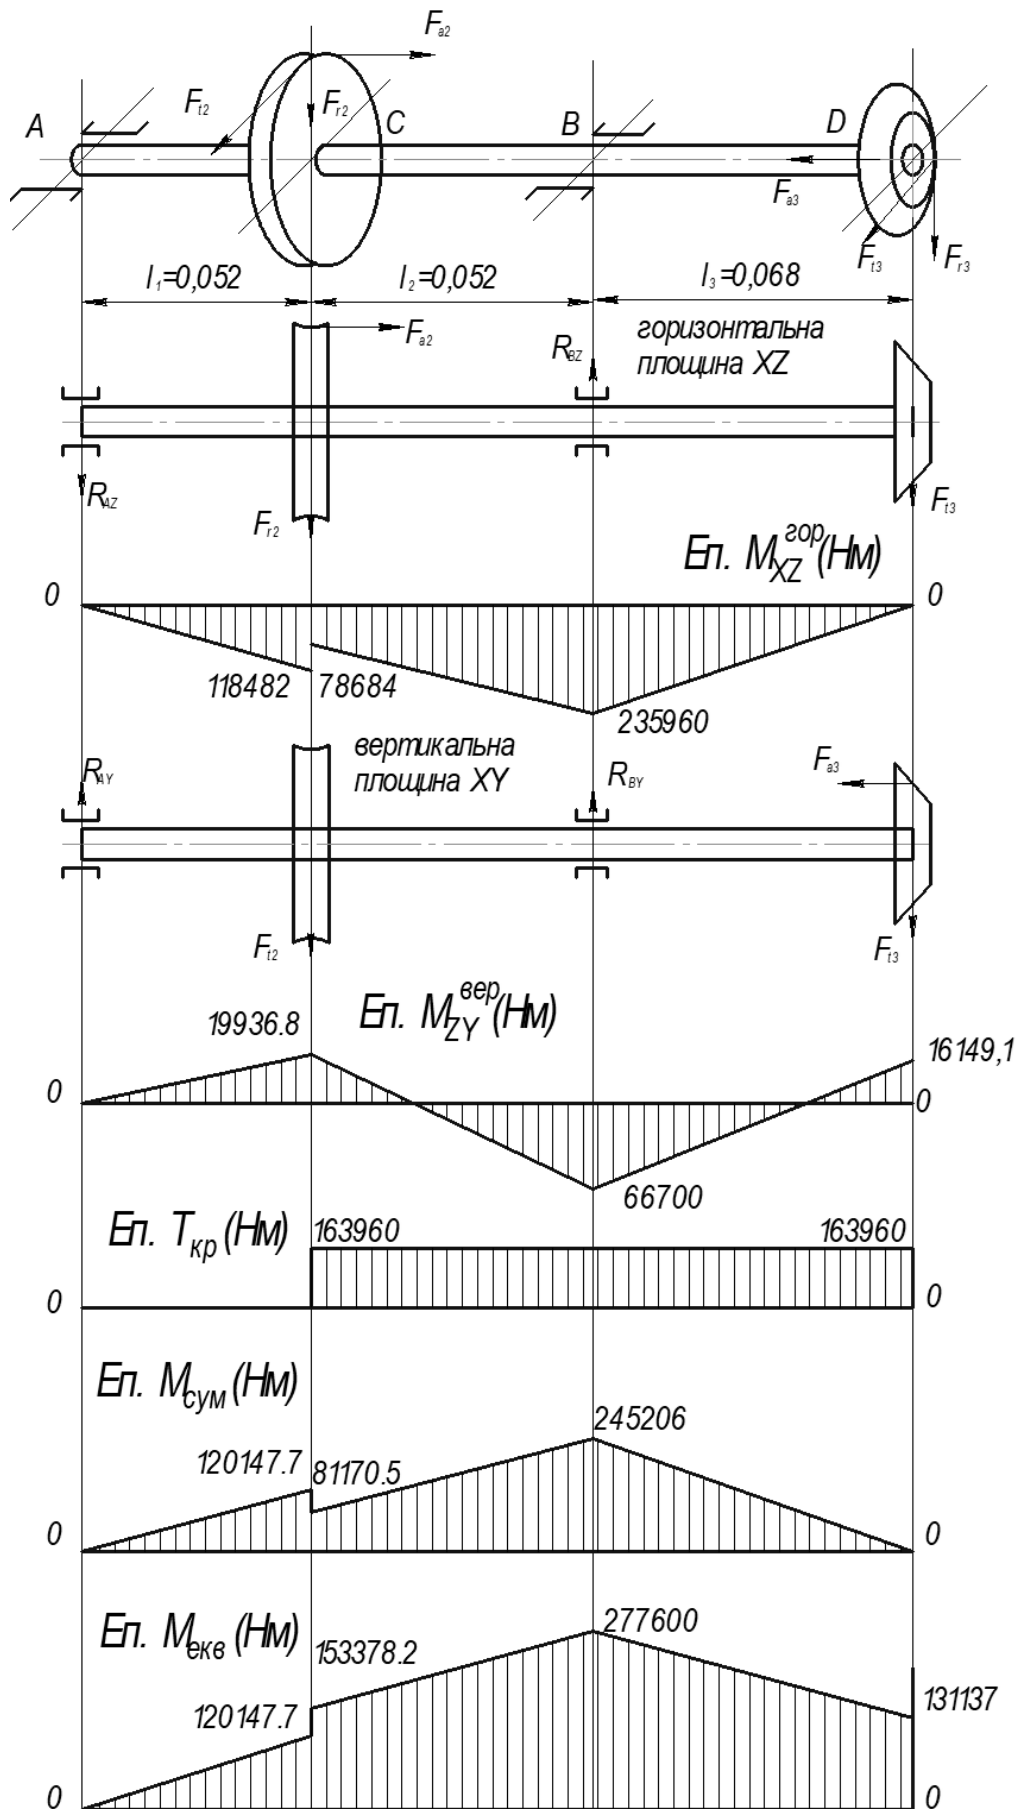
Епюри вала Колеса черв'яка і зубчастого колеса
